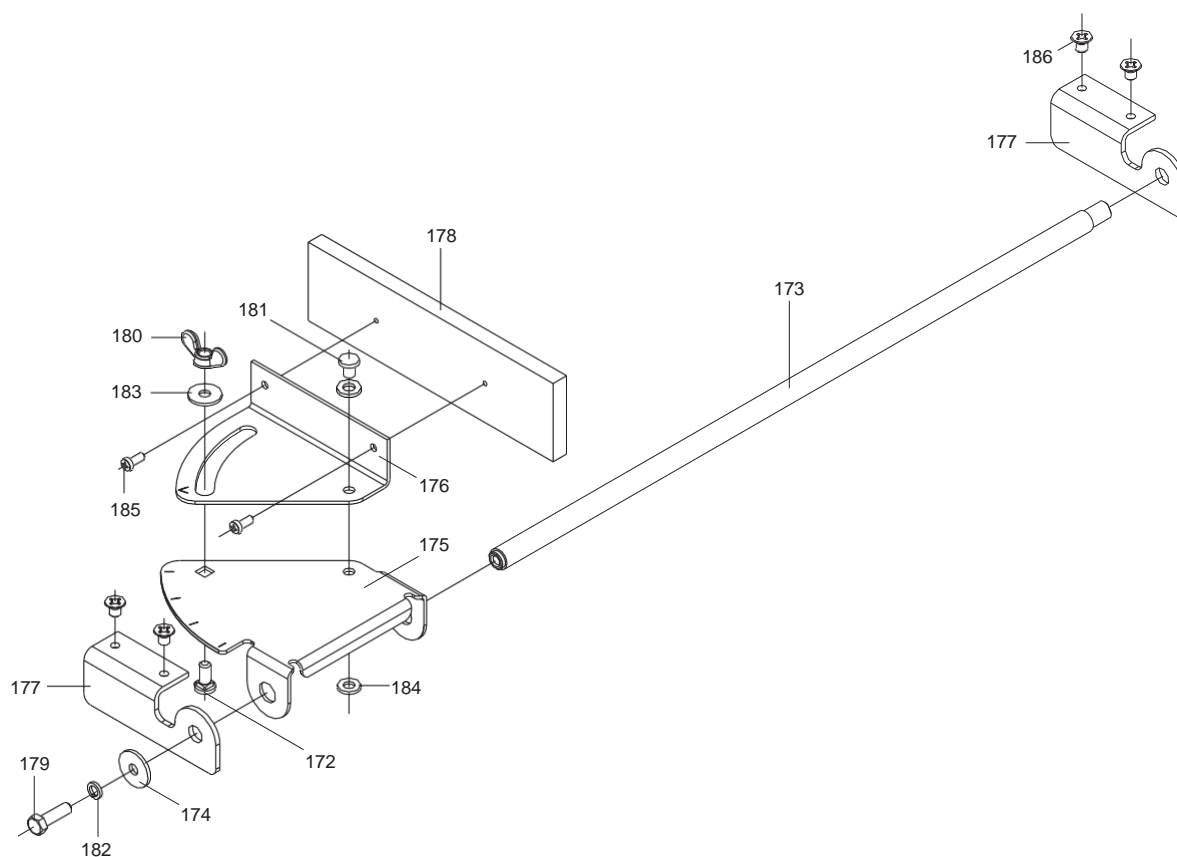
Приспособление для поперечной распиловки под углом 0000-04.
